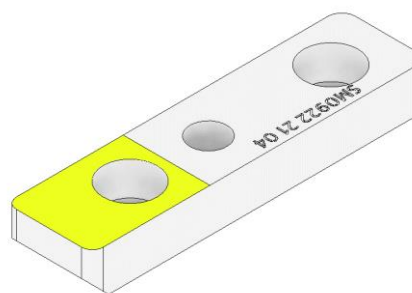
Univerzální základna přípravku    Obr. 7.2 – Univerzální základna přípravku
